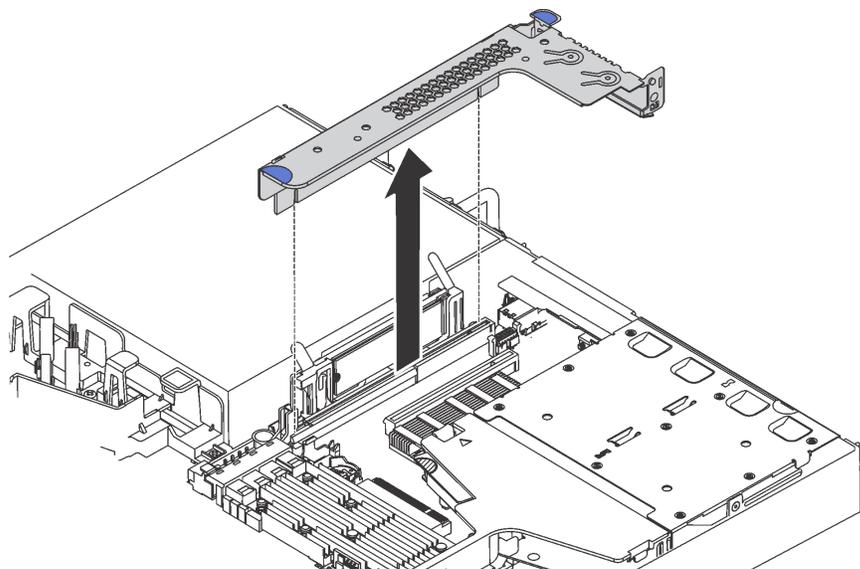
Entfernen der Adapterkartenbaugruppe
